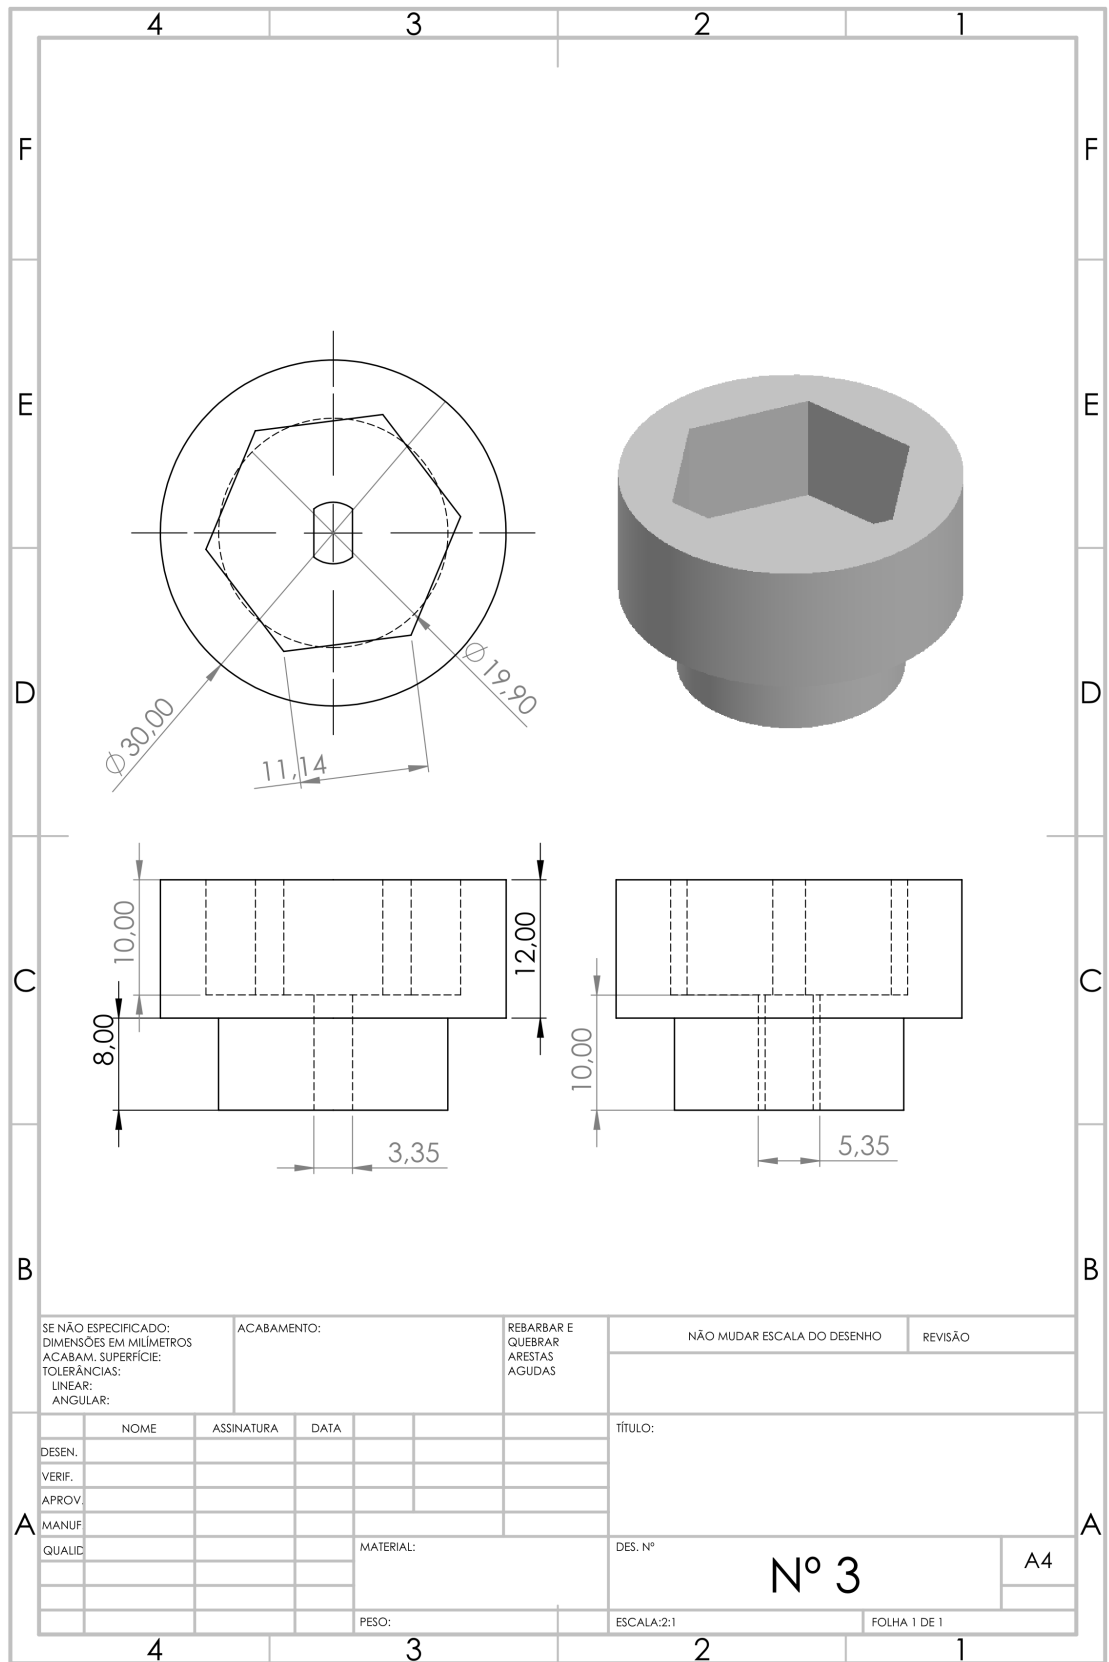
Desenho Técnico do Encaixe entre Eixo do Motor, Rolamento e Parafuso do Mandril
